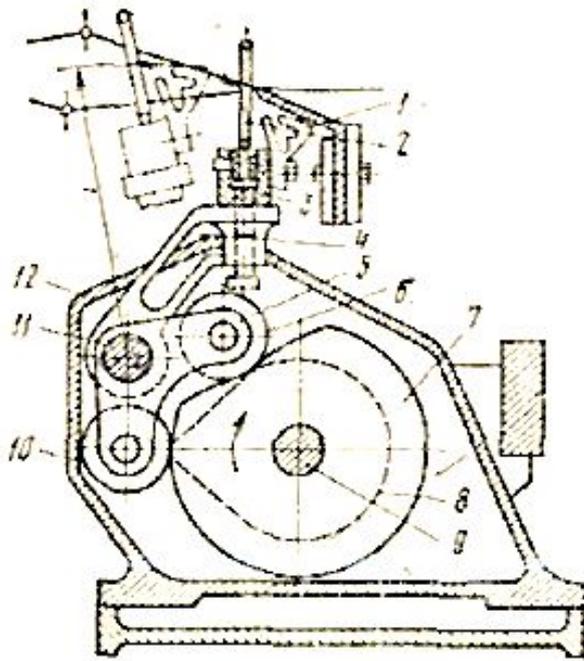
Батанный механизм станка СТБ: 1- зубья направляющий гребенки (канала) , 2- бердо, 3- брус батана, 4- лопасть, 5- двуплечий рычаг, 6 и 10 – парные ролики, 7 и 8 –парные кулачки, 9- главный вал, 11-подбатанный вал, 12- корпус батанный коробки.
